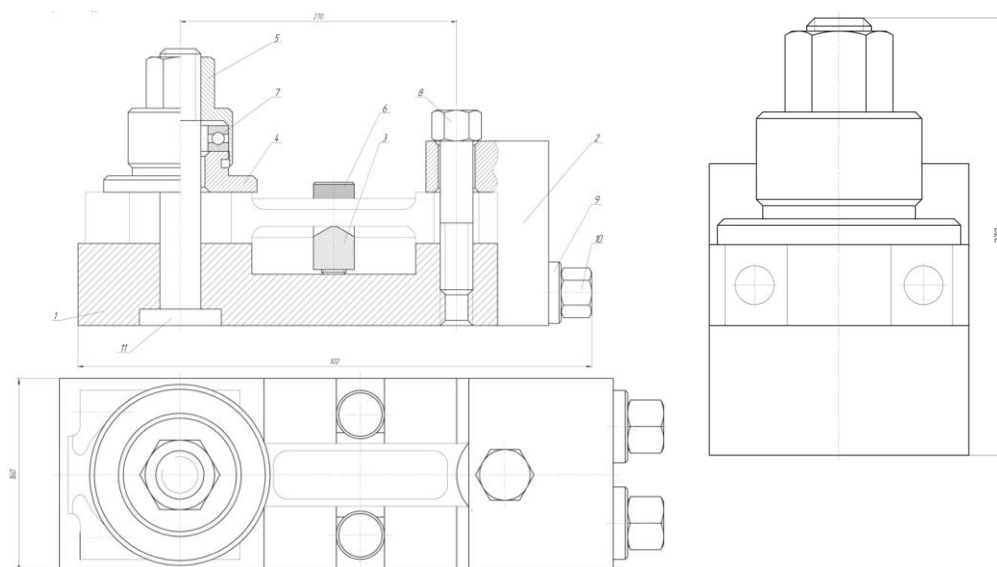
Ремонтное приспособление для правки стержней шатунов двигателей
